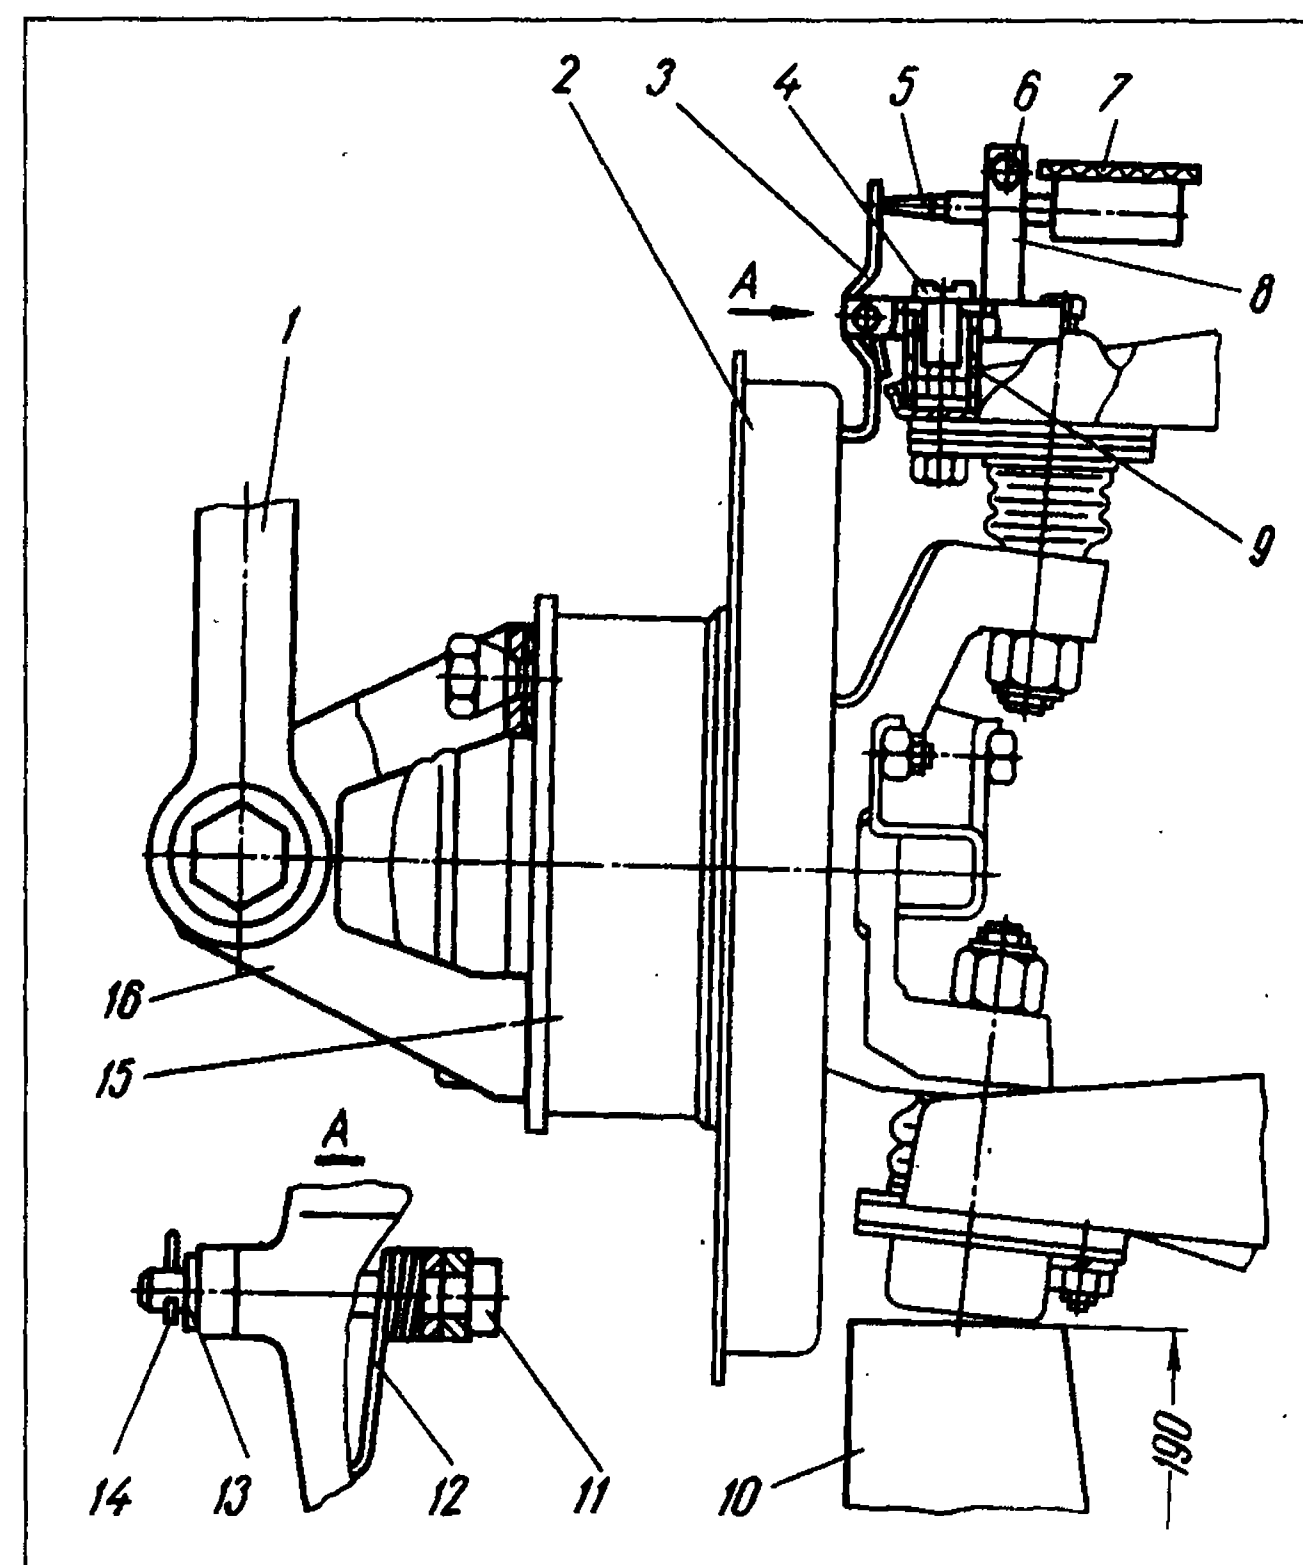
Замер зазора в верхнем шаровом шарнире приспособлением 02.8701.9500 (тормоз условно не показан):
